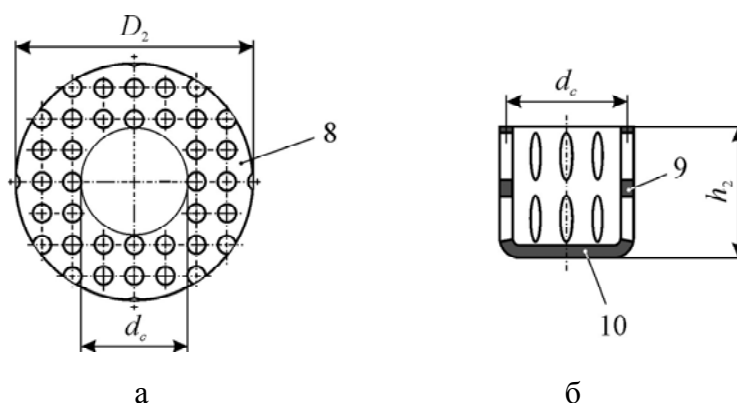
Заготовка (а) та деталь (б) після витягування за пунктом 2
